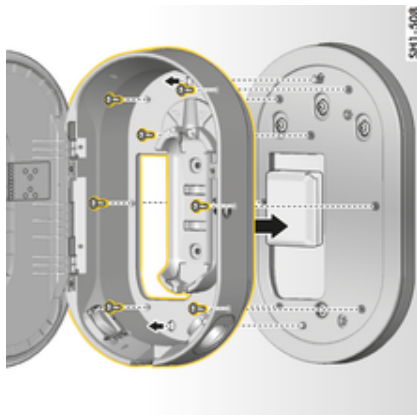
Atornillado del puerto de carga en la placa de montaje
